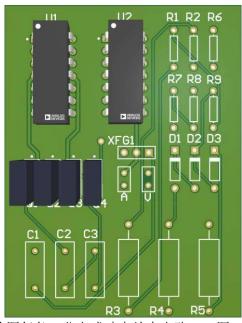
绘图任务一分立式功率放大电路 PCB 图 3D 效果图
